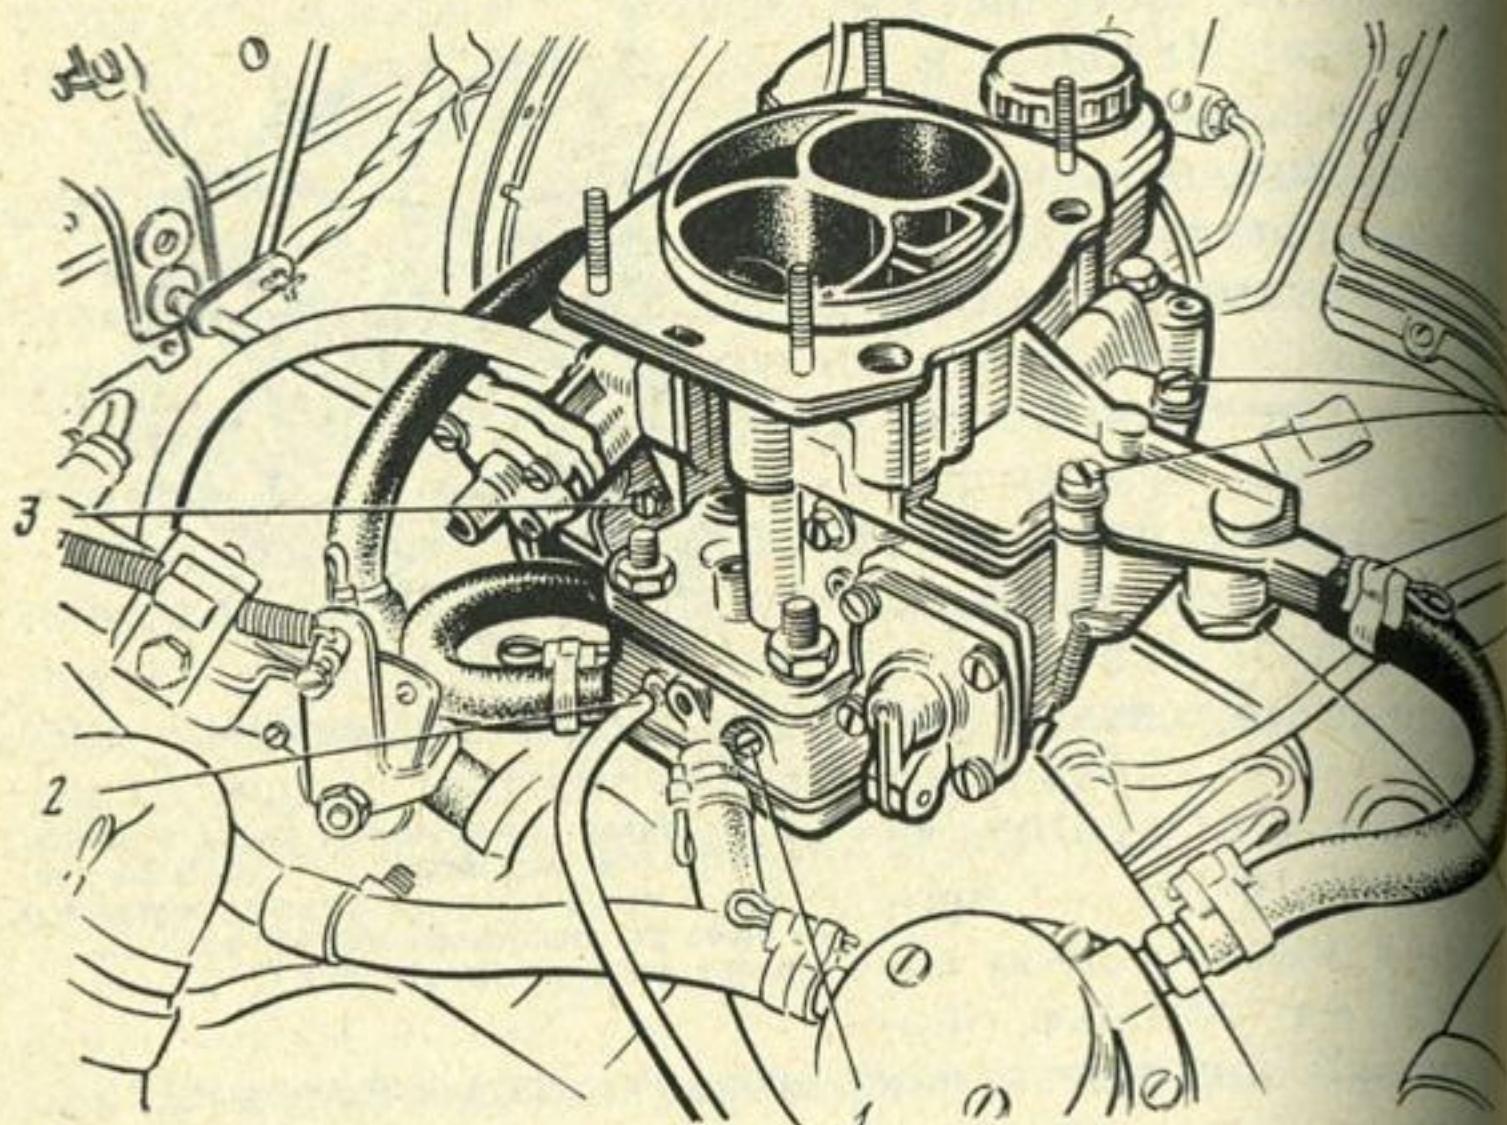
Карбюратор 2101-1107010-11, установленный на двигателе
